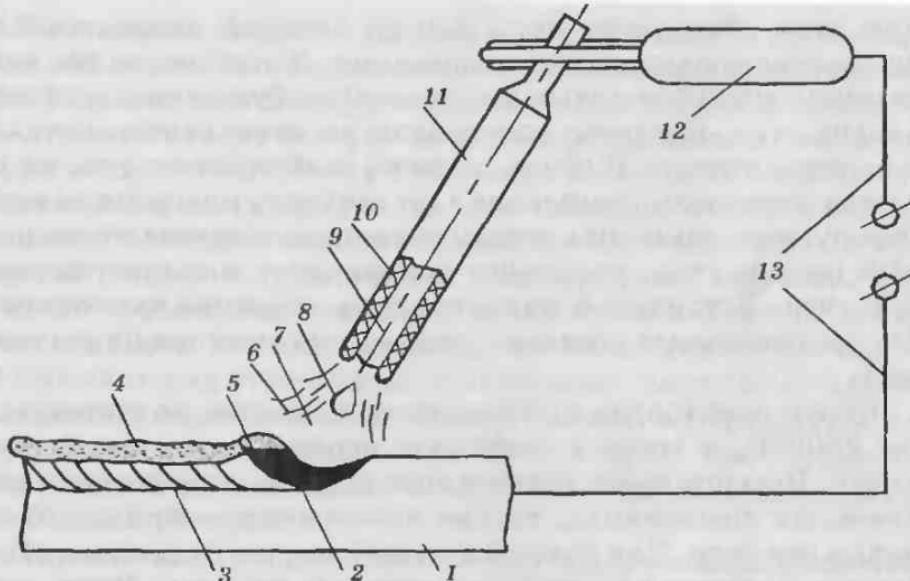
Схема ручной дуговой сварки:
